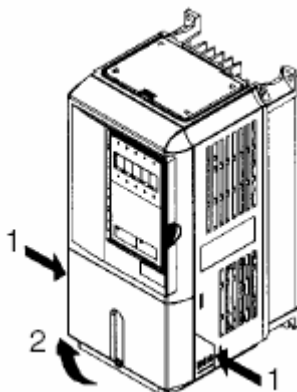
Desmontaje de la Cubierta de Terminales de Conexión.
